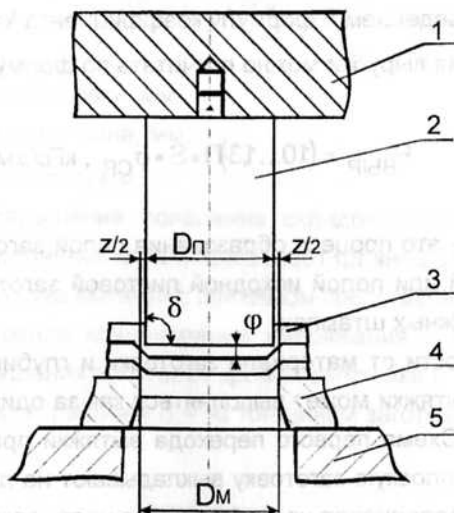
Схема вырубной заготовки в вырубном штампе:
